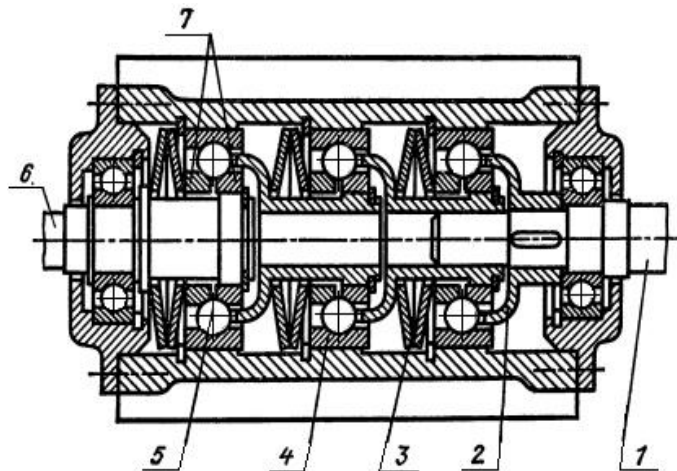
Трехступенчатый шариковый планетарный редуктор
